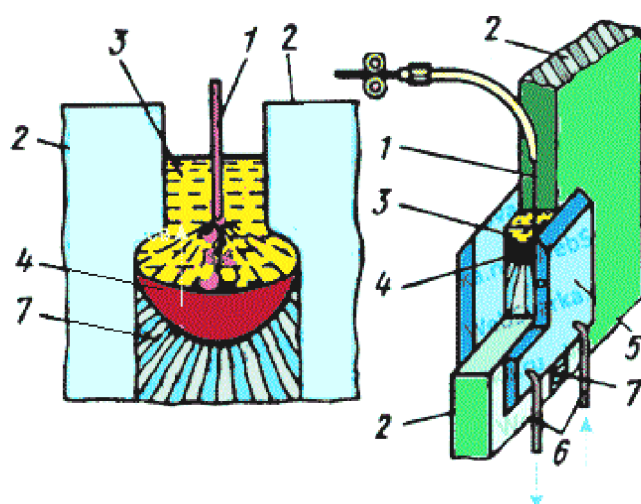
Принципиальная схема электрошлаковой сварки
